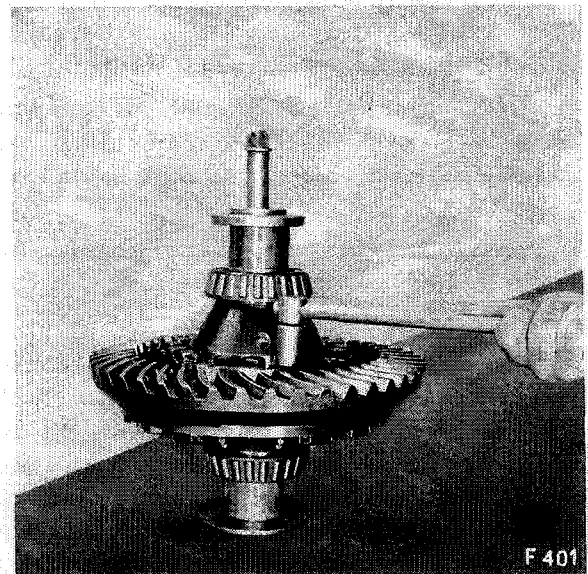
Lösen der Befestigungsschrauben für das Differentialgehäuse
